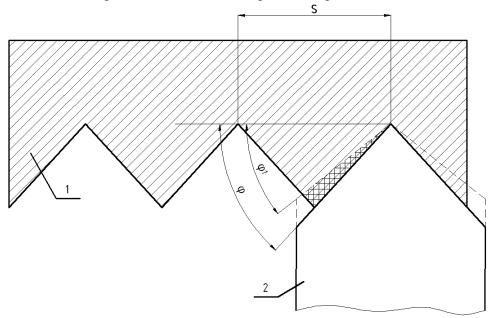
Влияние угла ϕ на шероховатость обработки поверхности: 1 – заготовка; 2 – резец
